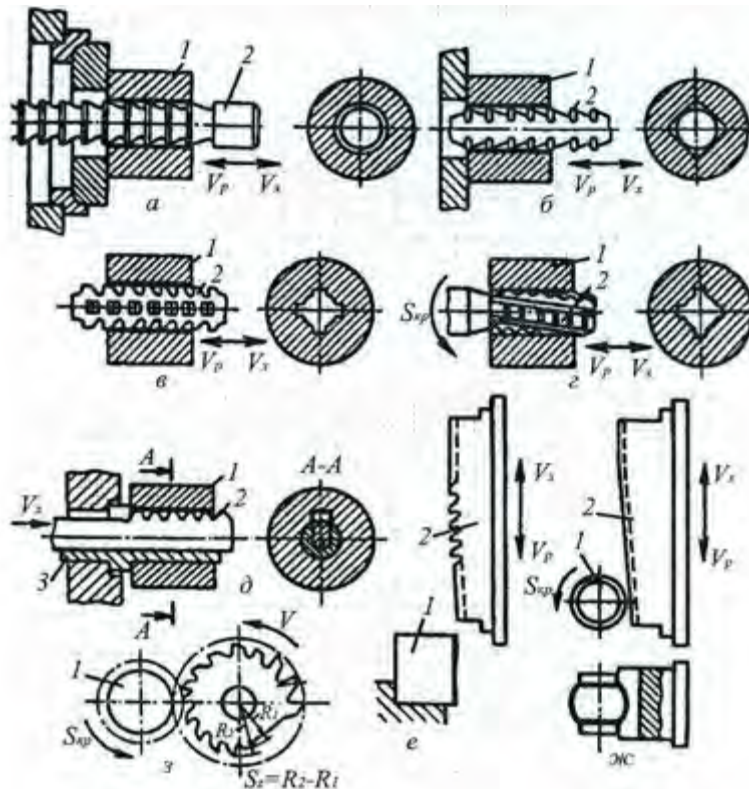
Схеми оброблення поверхонь заготовок на протяжних верстатах
